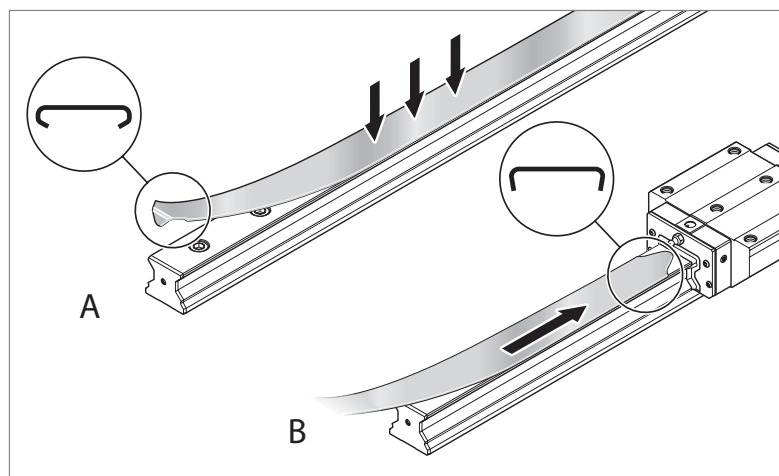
Nastro di protezione con sede fissa/parte scorrevole:
